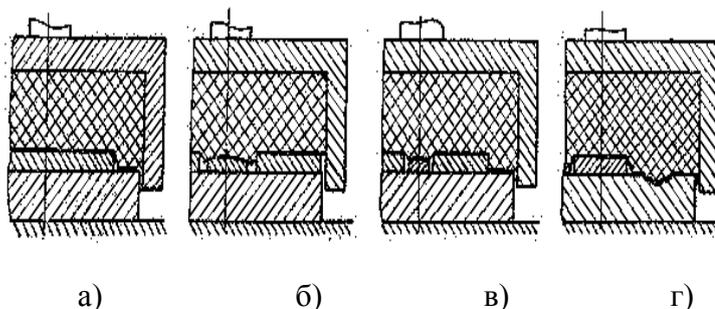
Схемы различных операций вырезки резиной: а – вырезка; б – пробивка; в – вырезка и пробивка; г – пробивка и формовка
